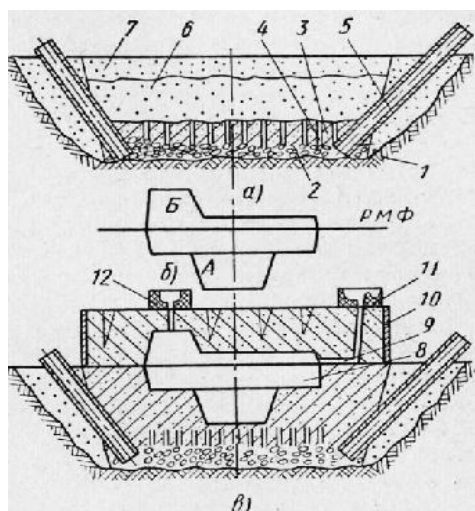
Закрытая почвенная формовка по твердой постели : а — приготовление
